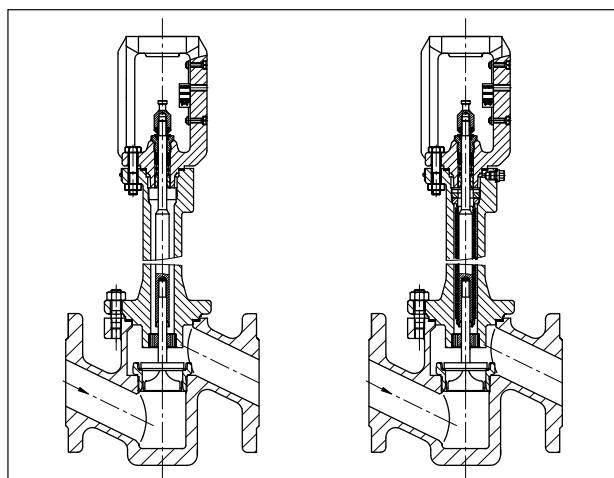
Ventil Typ 3241 · DN 15 bis 80 · Schmiedestahlausführung · links: mit Isolierteil, rechts: mit Balgeabdichtung
